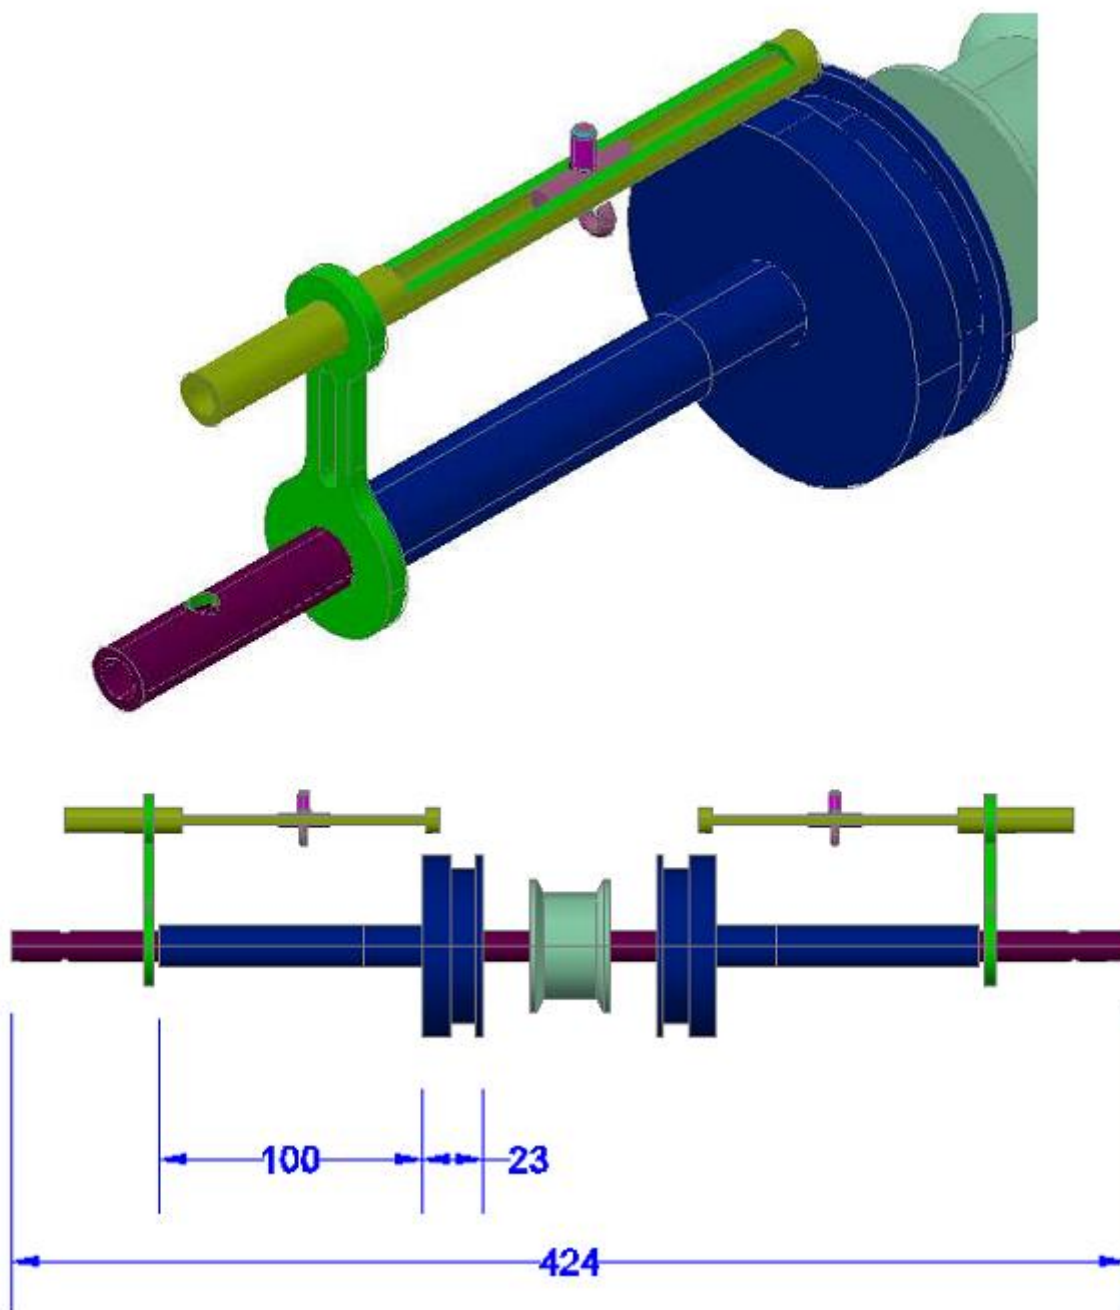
Загальний вигляд вузлів прядильної частини із габаритними розмірами
